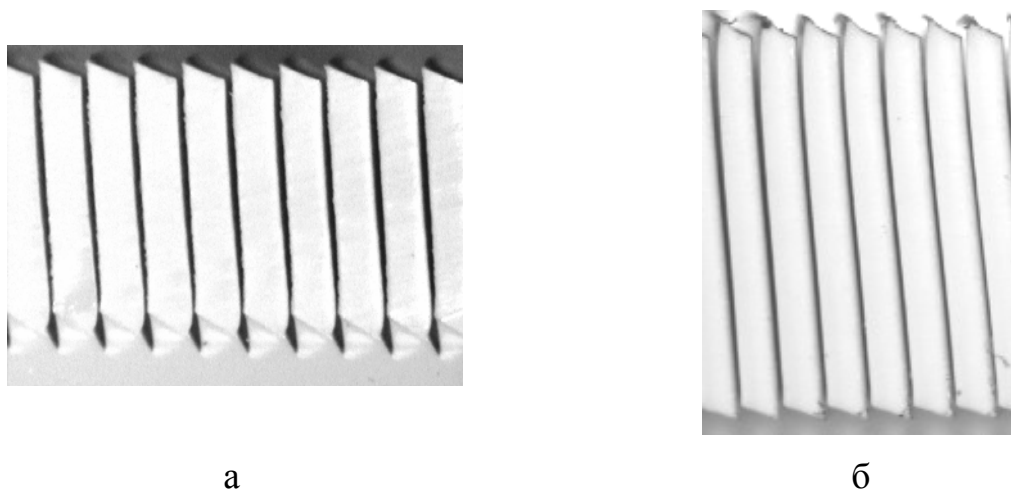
Щелевая структура фильтроэлемента с внутренними продольными пазами (а) и из заготовки кольцевого сечения (б)
